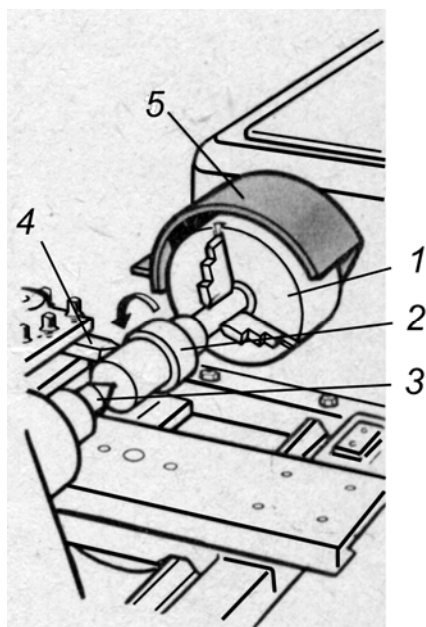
Схема закрепления заготовки в патроне с поджатием центром задней бабки:
